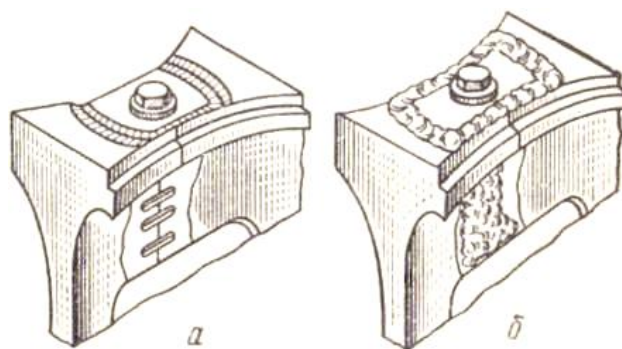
Підготовка тріщин в перемичці між циліндрами до заварки (а) і перемичка після заварки (б).
